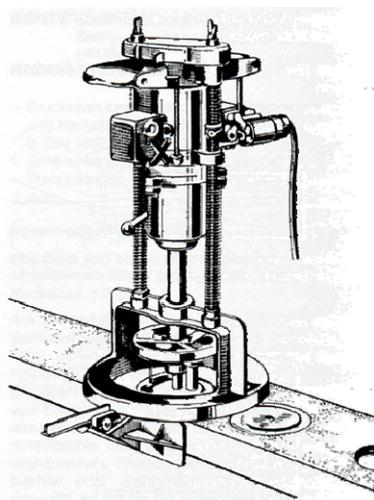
Bohrgestell mit Ringdübelwerkzeug [7]
